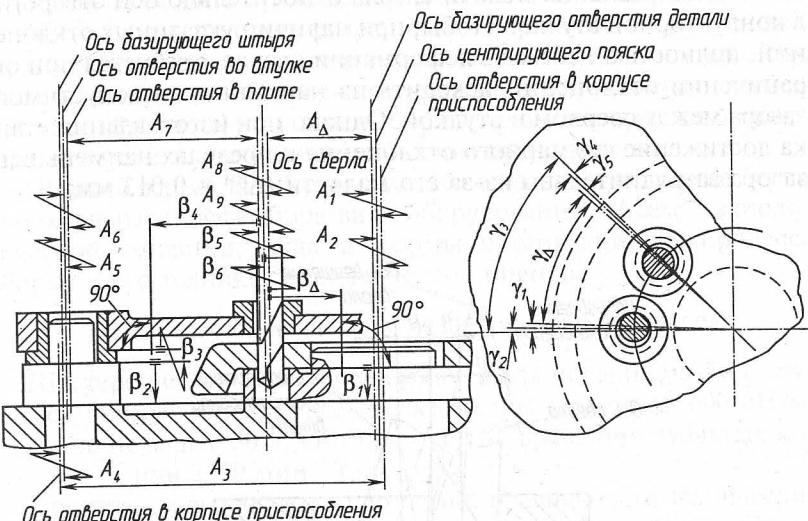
Схема размерных цепей системы станок — приспособление — инструмент — заготовка агрегатного станка, с помощью которых достигается точность положения одного из обрабатываемых отверстий
